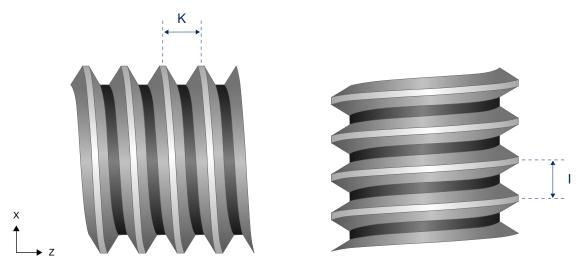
Angabe der Gewindesteigung bei Längsgewinde
